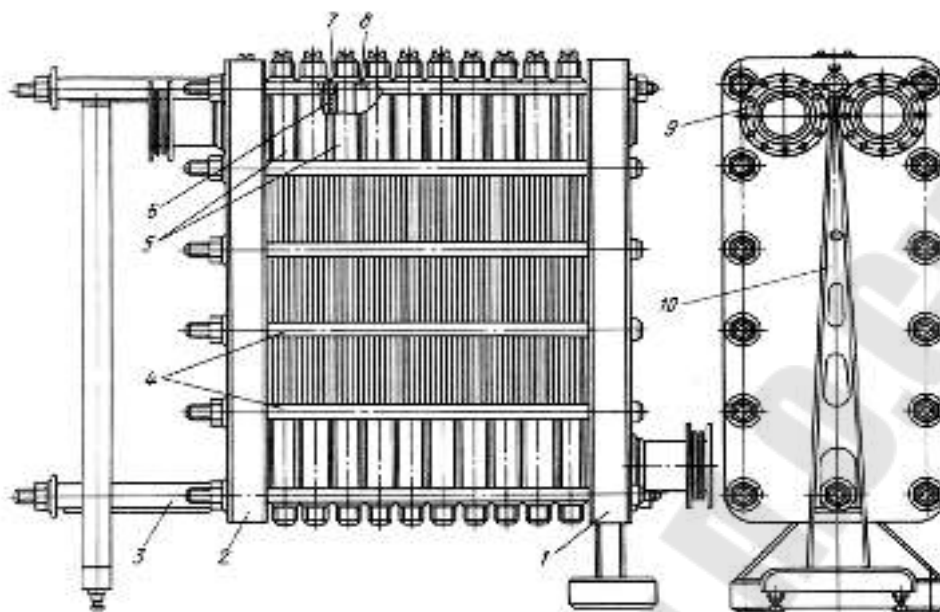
[2]. Пластинчатый теплообменник: 1 – неподвижная плита; 2 – подвижная плита; 3 – нижняя штанга; 4 – стяжные болты; 5 – сварные блоки пластин; 6 – глухая втулка; 7 – кольцевая прокладка; 8 – проходная втулка; 9 – верхняя штанга; 10 – стойка
